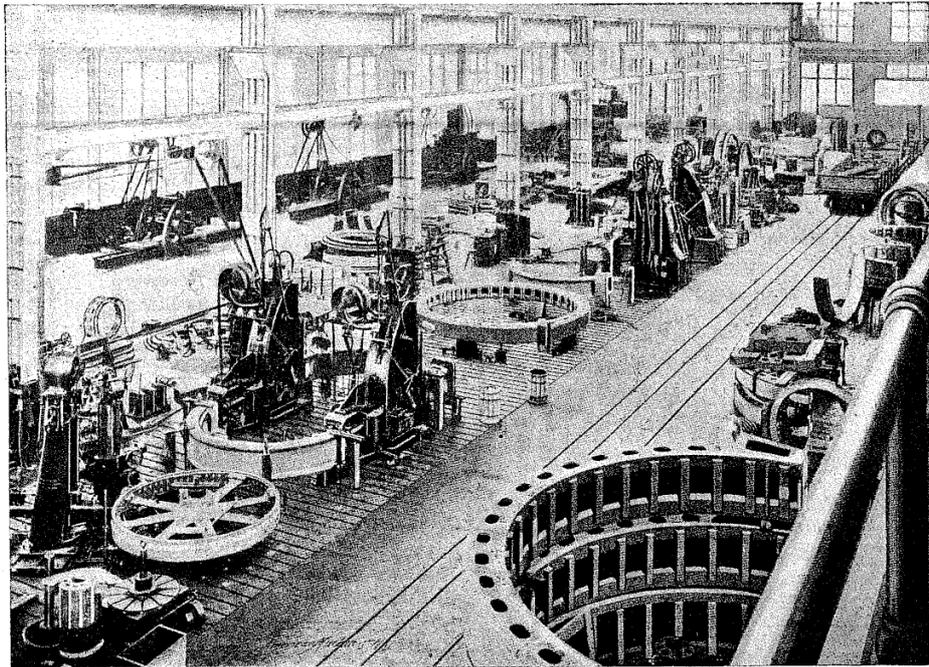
Ateliers de Shenectady, 2^e groupement.
